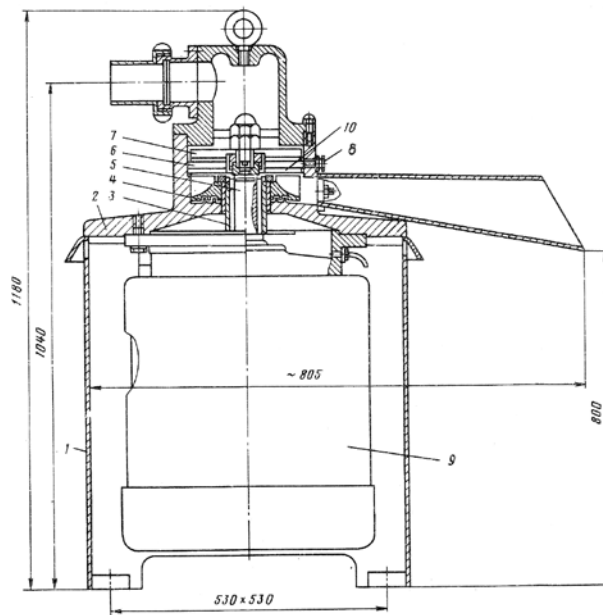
Емульситатор К6-ФИ2-М: 1 - станина; 2 - циліндричний корпус; 3 - маточина; 4 - розвантажувальний диск; 5 - вал електродвигуна; 6 - нерухома ножова гратка; 7 - рухомий ніж; 8 - фіксуючий гвинт; 9 - електродвигун; 10 - підпорка
